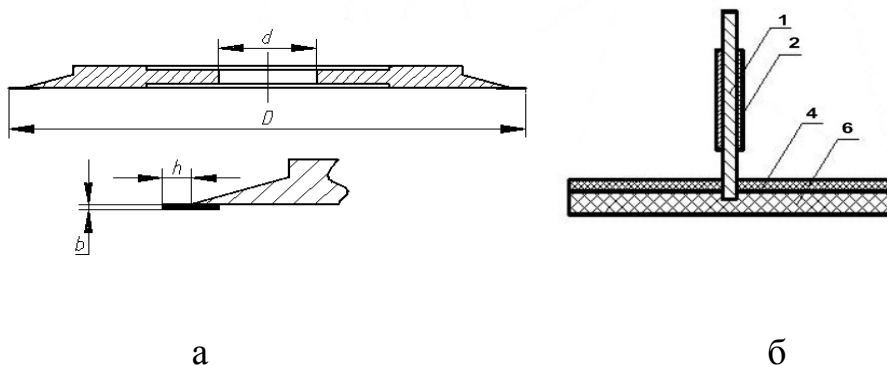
ДАР (а): b – толщина лезвия; h – высота лезвия; d – посадочный диаметр; D – внешний (рабочий) диаметр и схема резки пластины (б)
